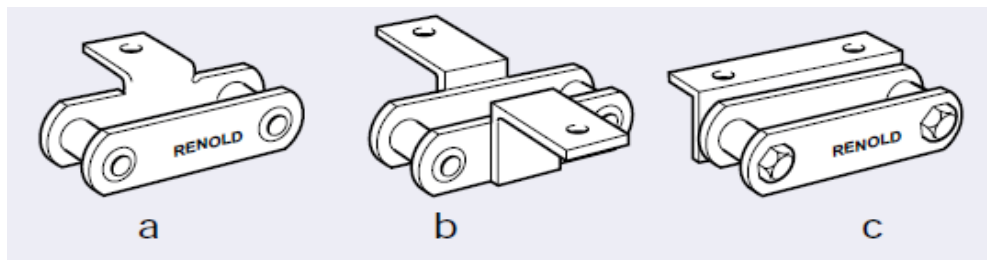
Accesorios tipo K. a) K1, accesorio doblado, b) K1, soldados a la placa de unión y c) K2, atornillado a través del pasador hueco.
